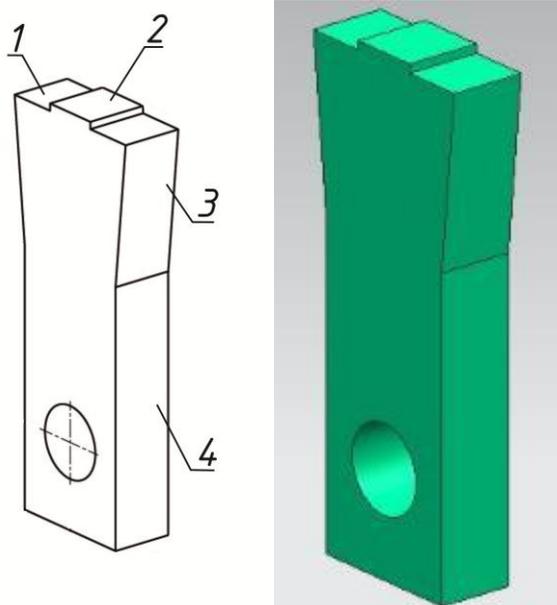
Предлагаемый шарнирно закрепленный молоток молотковой шахтной мельницы.
